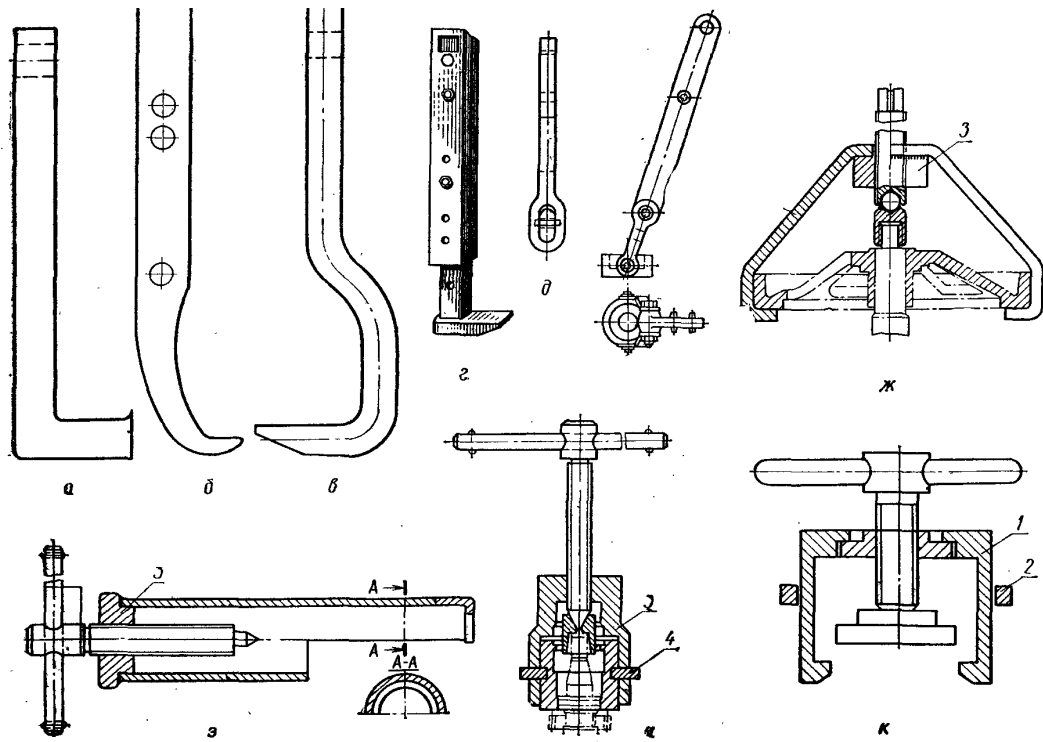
Захвати різної форми: а, б і в - лапчасті прості; г-лапчасті розсувні; д і е - захвати тяги; ж і з - жорстко з'єднані з корпусом; та і до - складові нерухомі; 1 – захват; 2 – кільце; 3 – корпус; 4 - вилка
